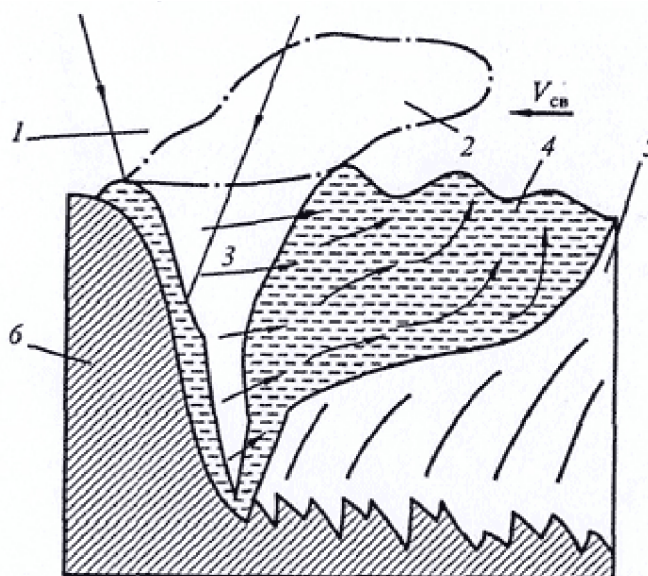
Схема сварочной ванны при лазерной сварке: 1 – лазерный луч; 2 – плазменный факел; 3 – парогазовый канал; 4 – хвостовая часть ванны; 5 – металл шва; 6 – свариваемый металл
